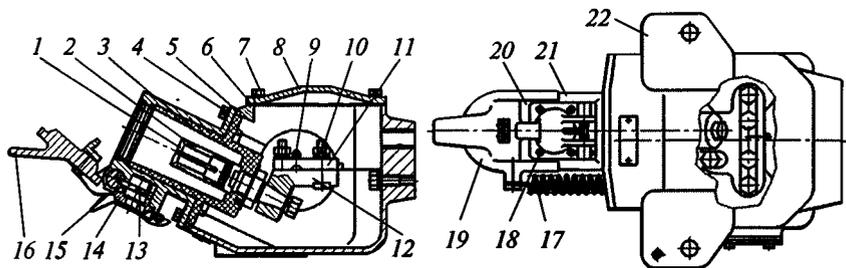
Розетка MBC-0-P-185-4000/800:
